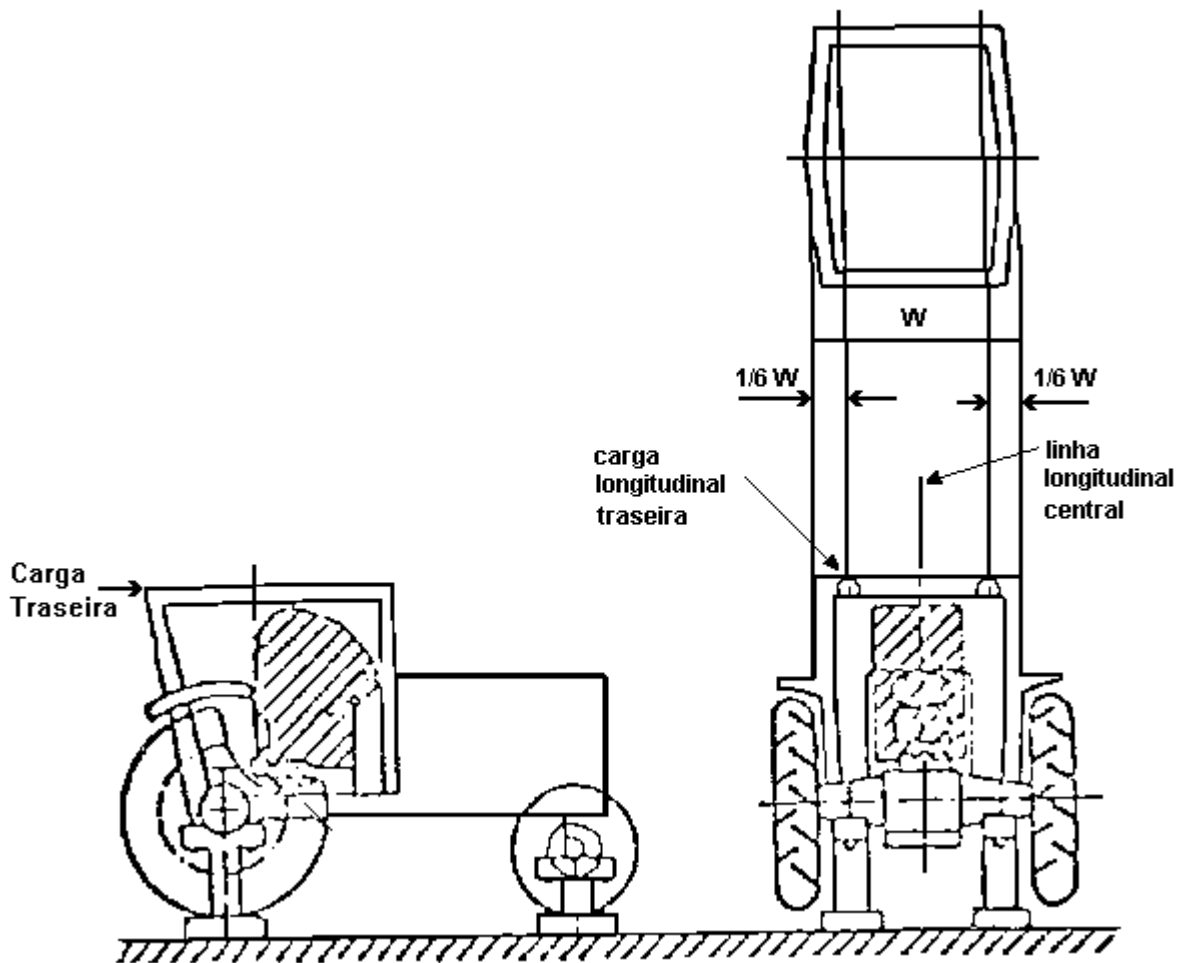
Ponto de aplicação da carga traseira.
